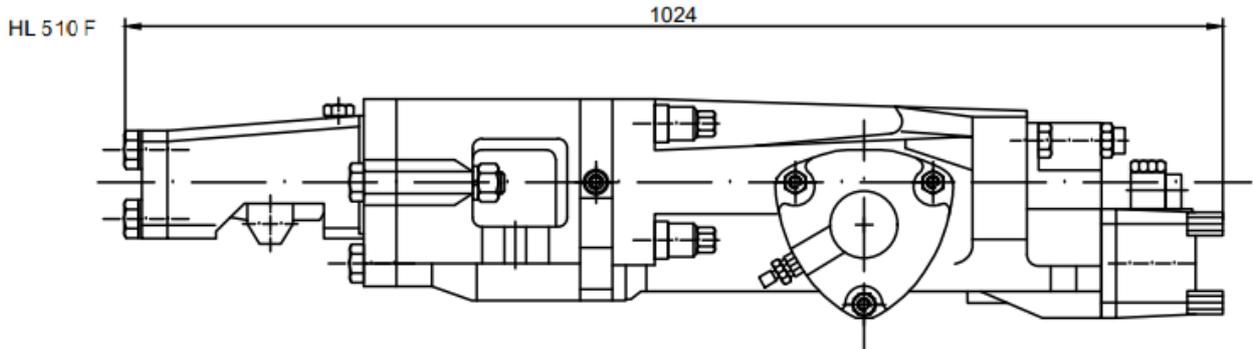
схема передвижного гидроперфоратора HL510 F.
